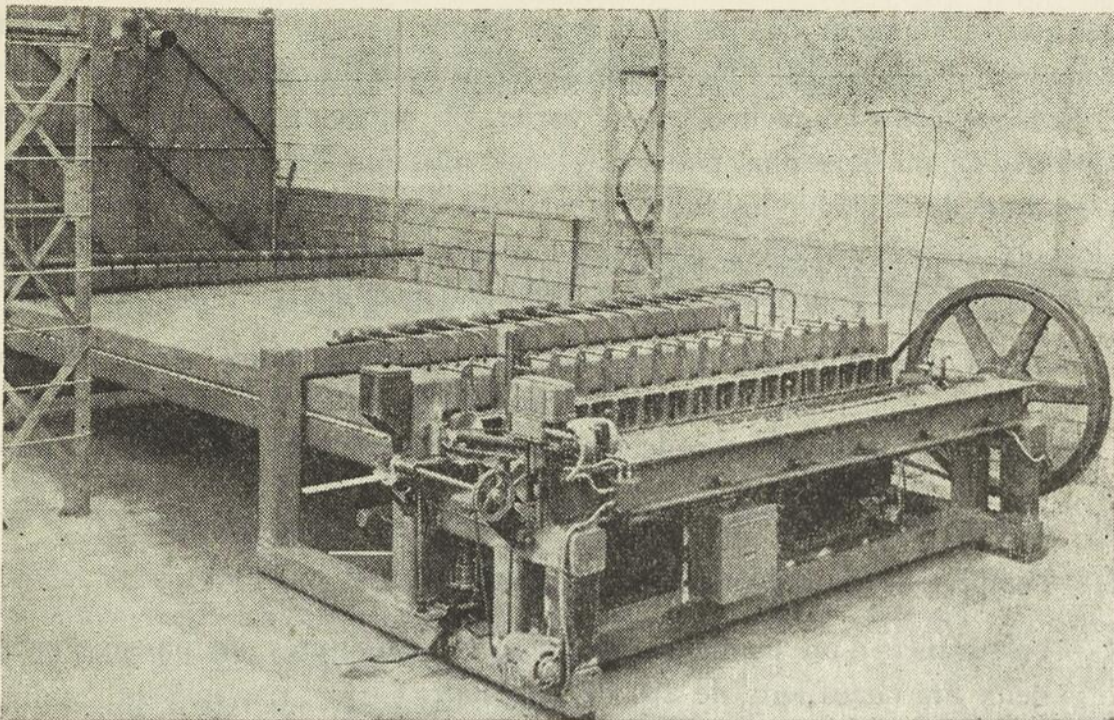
Vue d'ensemble de la machine. Entrée, côté d'alimentation. C'est volontairement que les capots de protection ont été enlevés afin de mieux montrer les divers détails de la machine. (Document H. BRENNELSEN et Cie, Paris.)
